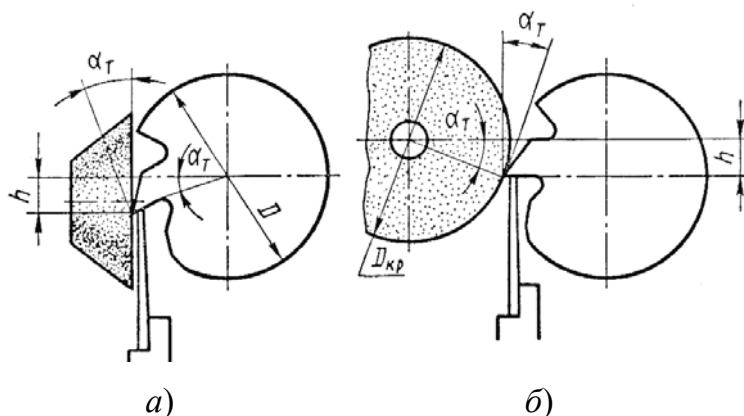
Установка абразивного инструмента при заточке задней поверхности обрабатываемого инструмента:
